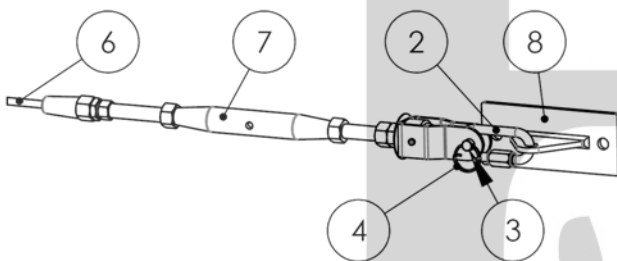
Método de montaje del tensor con la placa de anclaje final.
